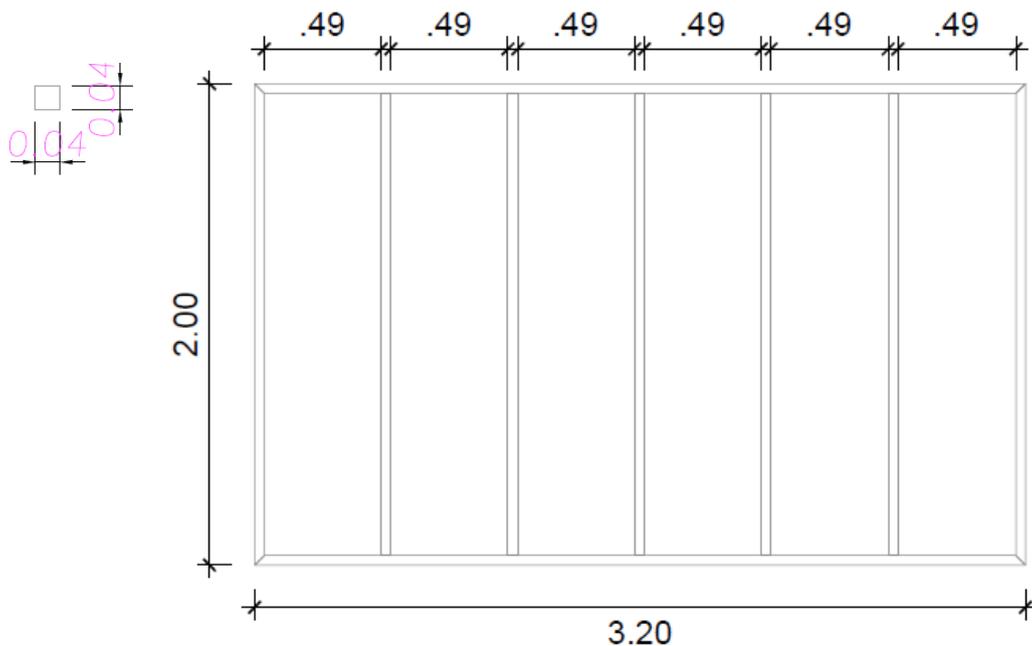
Vista frontal armado de puerta corrediza con tubo cuadrado.
